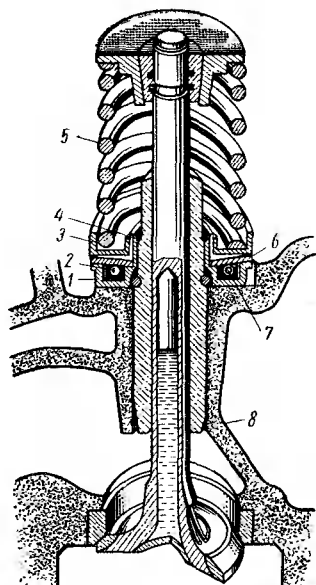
Механизм поворота выпускного клапана двигателей ЗИЛ-130:
